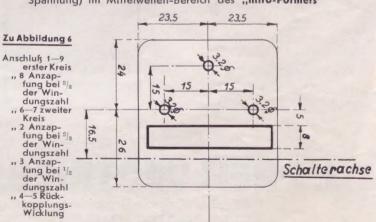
Ausschnitt im Chassis für Senkrecht-Montage der "Preh-Former"
